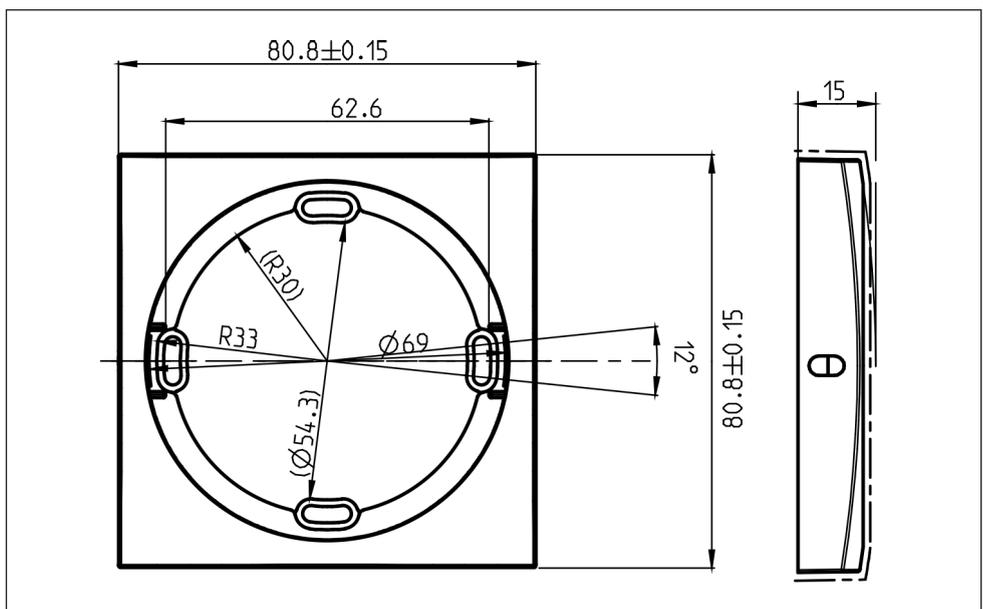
Maßblatt Rahmen (Draufsicht und Seitenansicht)
